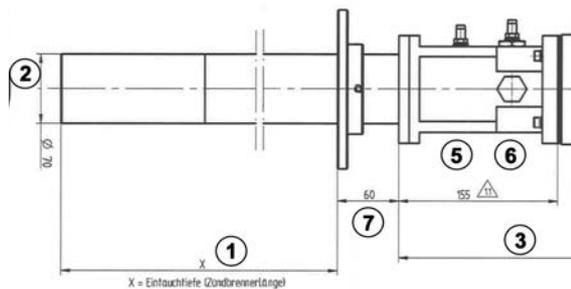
Dimensiones del quemador de ignición GFI70, variante C
